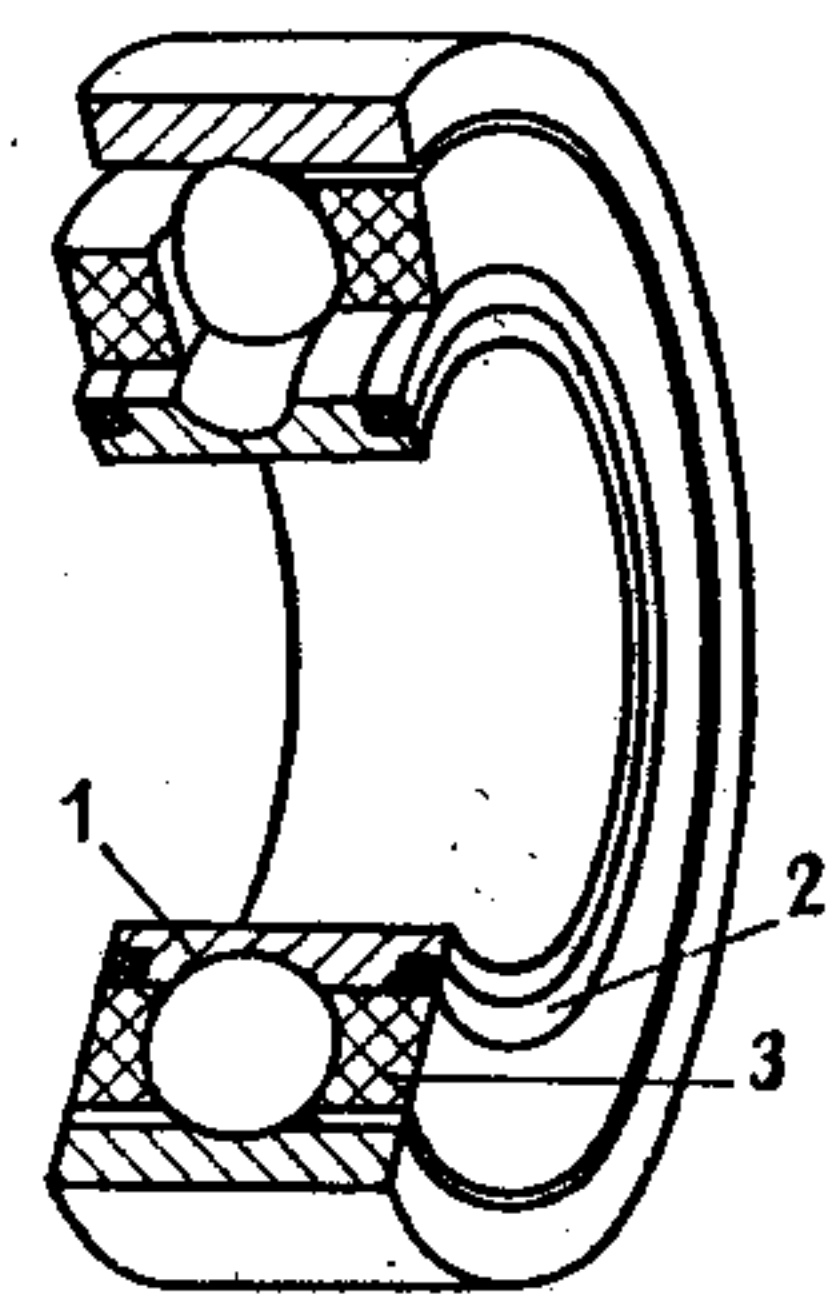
Шарикоподшипник с сепаратором и вставкой из полиамида: 1 — внутреннее кольцо подшипника; 2 — вставка; 3 — сепаратор
